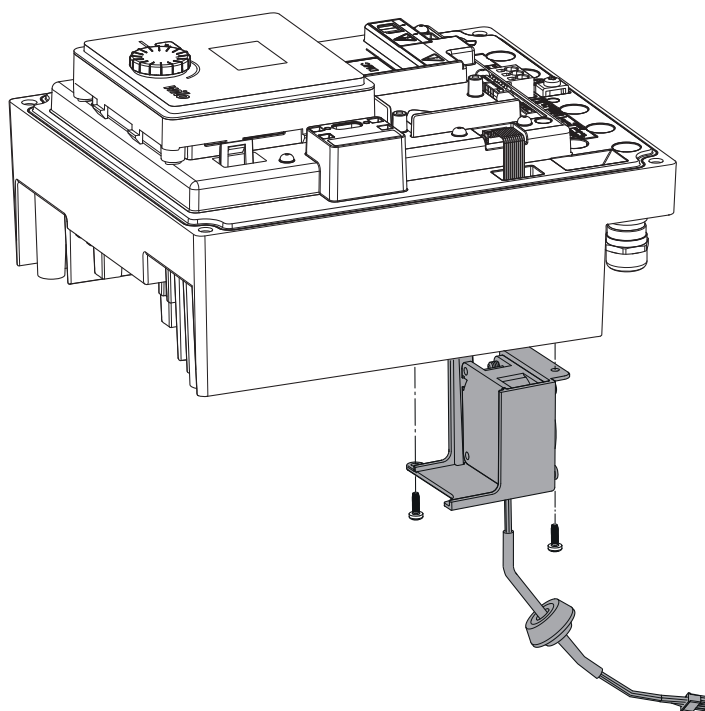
Retirer le ventilateur du module, ainsi que le câble et le joint en caoutchouc
